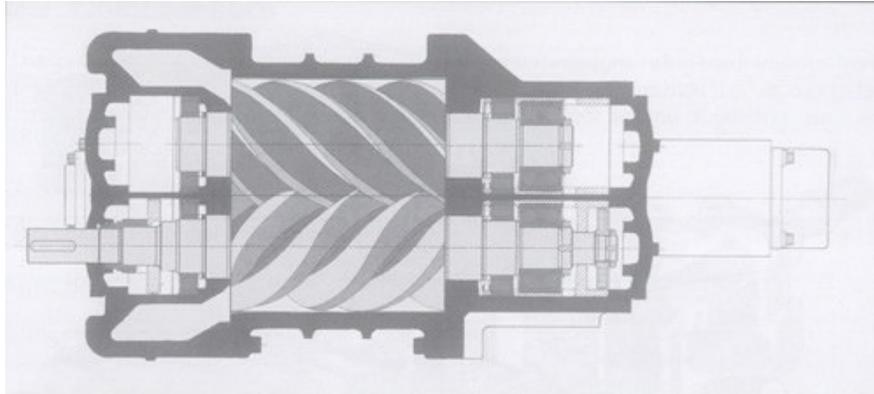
Esquema de compresor de doble tornillo rotativo.
